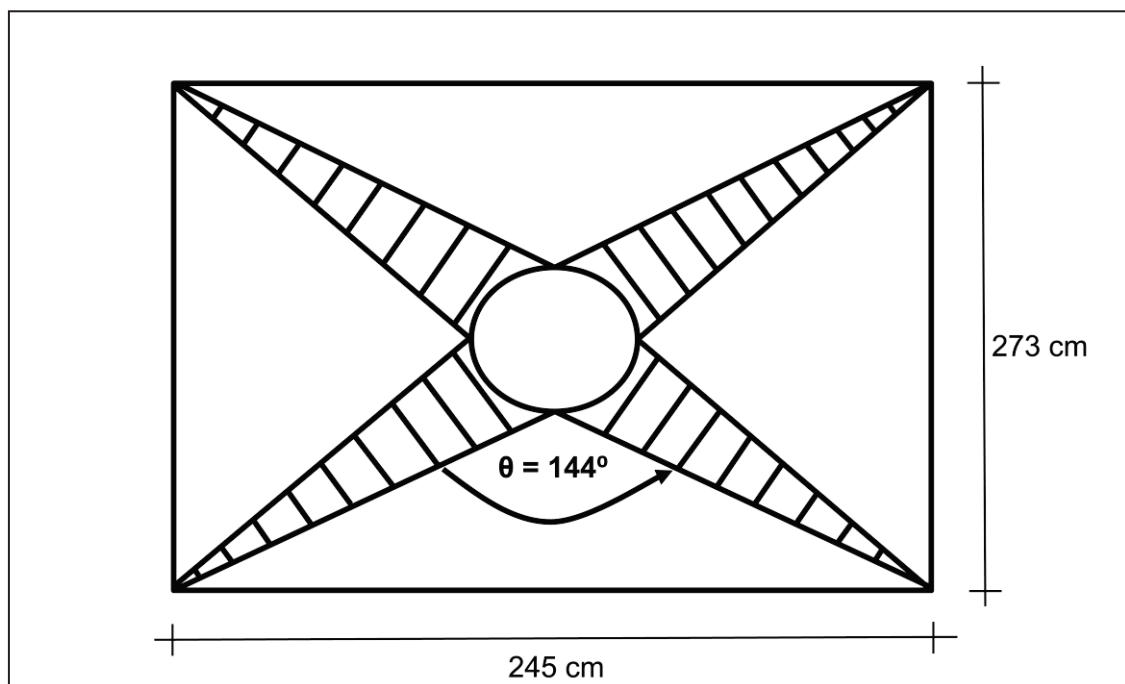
Dimensiones de la campana de extracción (vista en planta)
